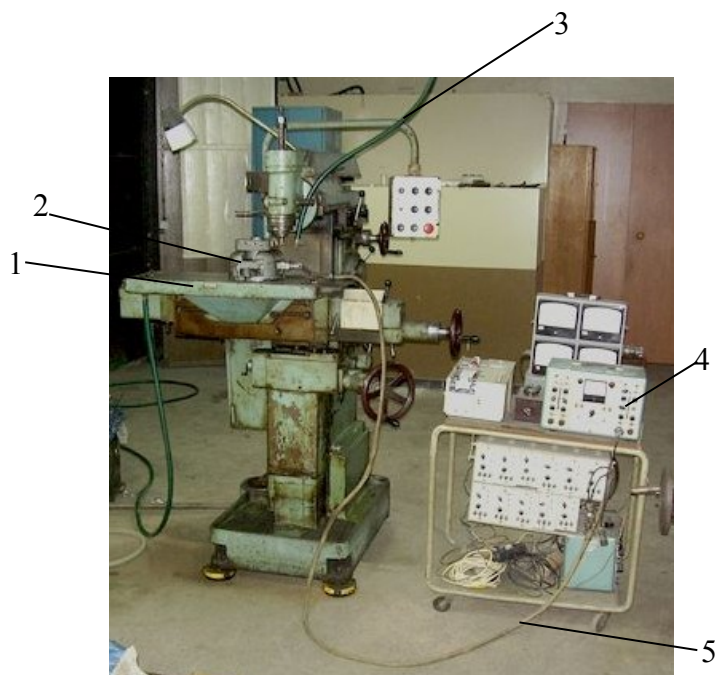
Общий вид стенда для проведения экспериментальных исследований (1 – фрезерный станок 6М76П-1; 2 – динамометр УДМ600; 3 – устройство принудительного удаления стружки; 4 – регистрирующий комплекс; 5 – линии передачи
